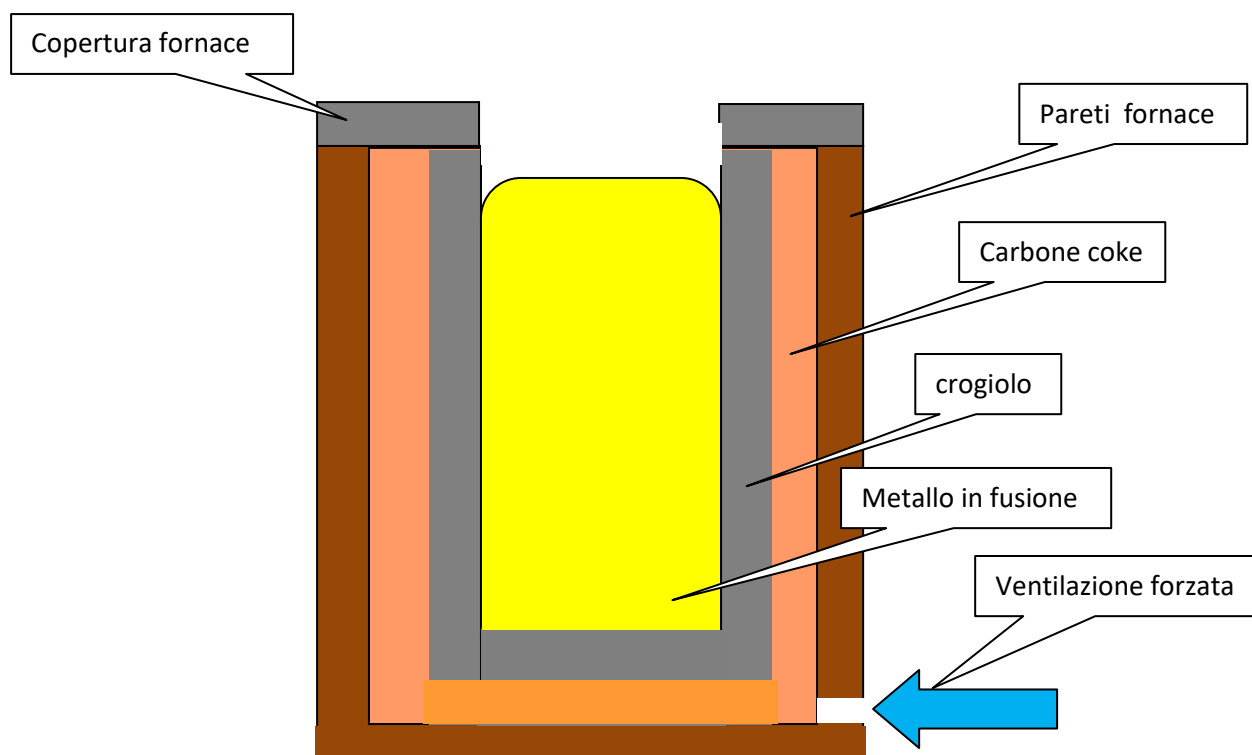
struttura di una attuale fornace utilizzata per piccole quantità di metallo. Durante il processo di fusione viene spostata la copertura per immettere ulteriore carbone per alimentare la combustione.
